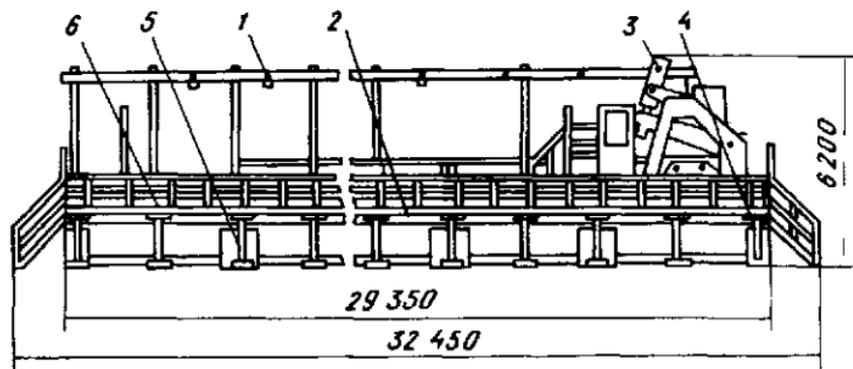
Агрегат СМЖ-541 для разрушения некондиционных железобетонных изделий
